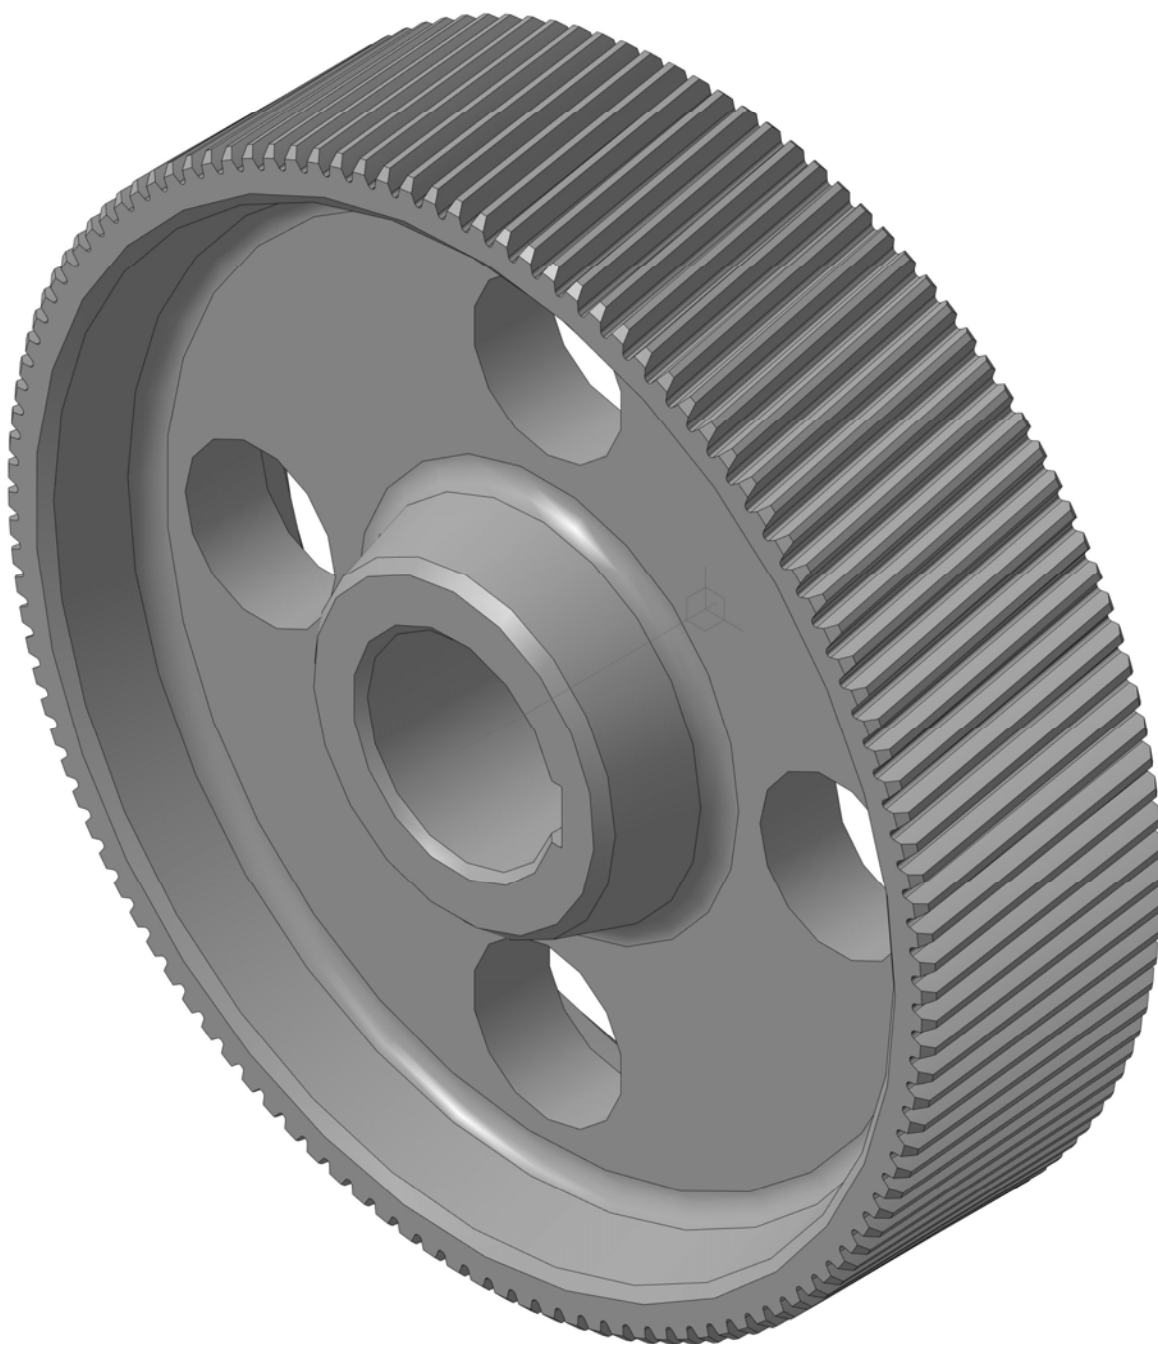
Cad-модель циліндричного зубчастого колеса
